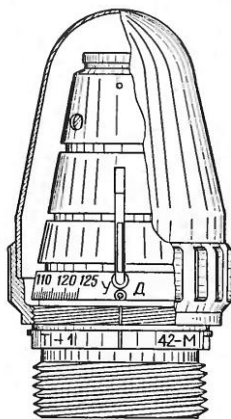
Трубка Т-1 (загальний вигляд)
